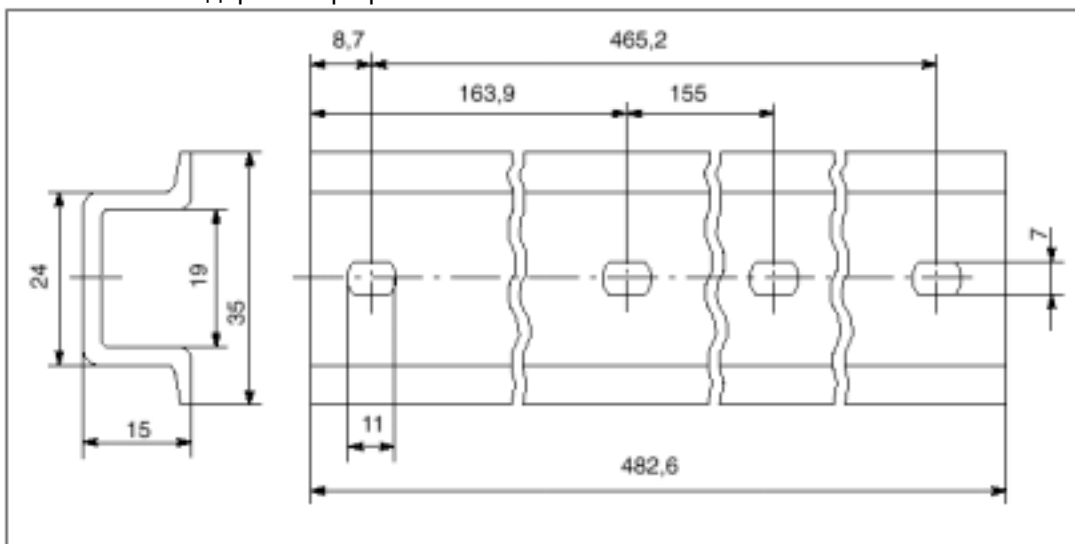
Чертеж с размерами 483-миллиметровой стандартной профильной шины.
